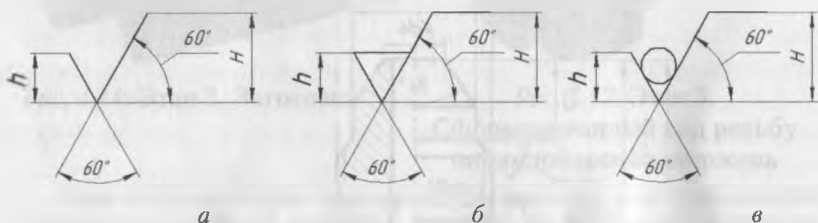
Знаки шероховатости, указывающие на вид обработки поверхности:
